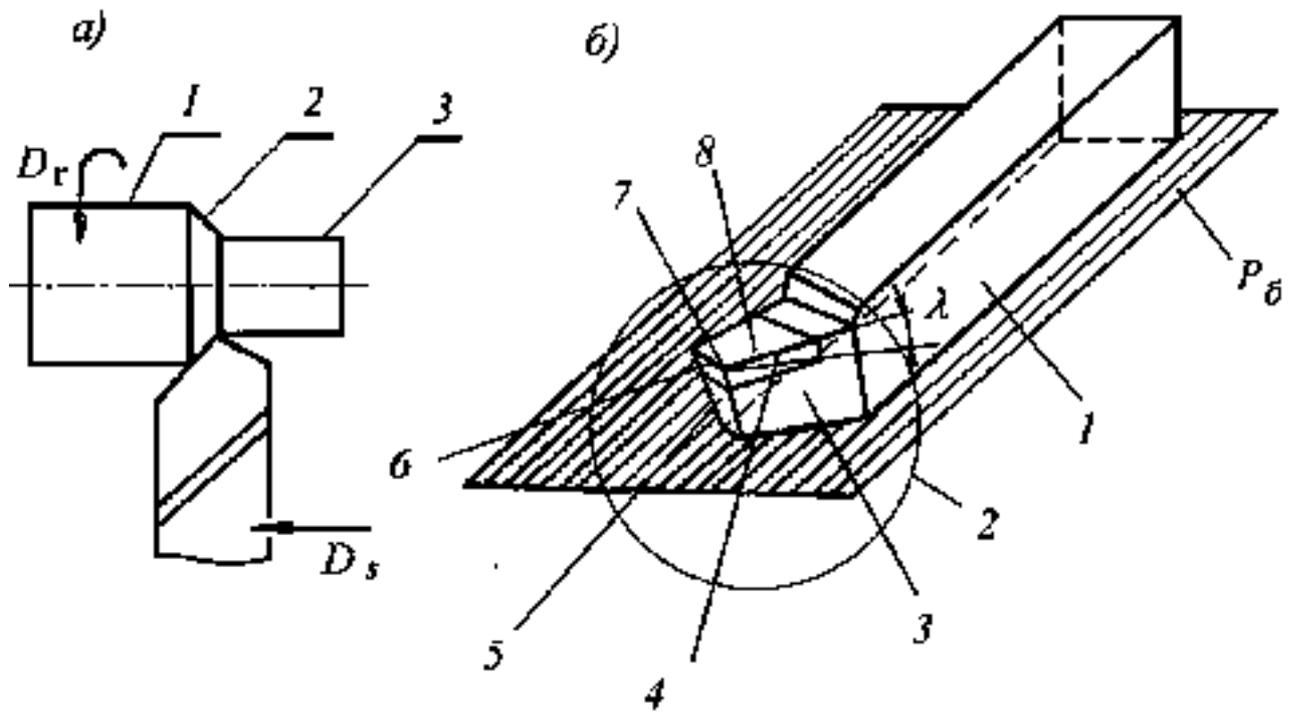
Схема точения (а), токарный проходной резец (б)
